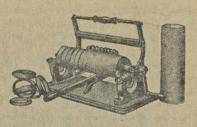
Аппараты для закатки рулонов и для резки рулонов на кольца
